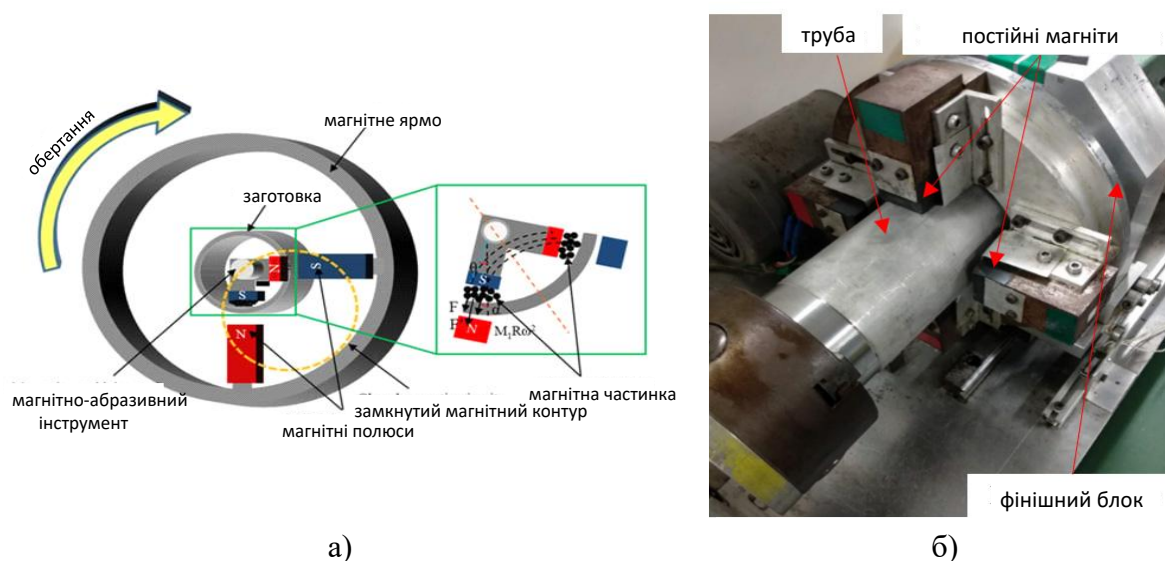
Схеми MAO для оброблення внутрішніх поверхонь труб великого діаметру [33]
